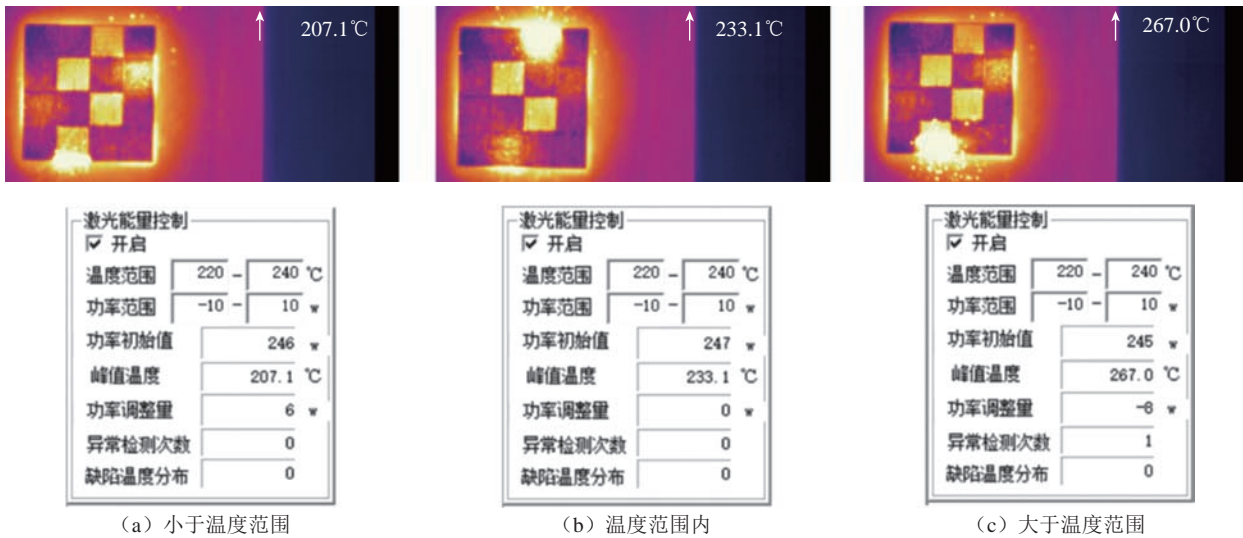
HUST 3D Print Master 软件中基于能场的路径规划方法
